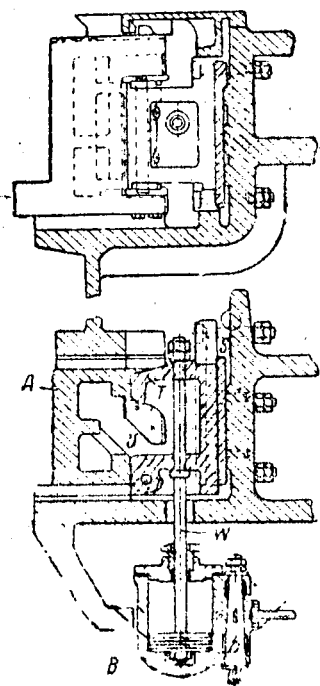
Общий вид кинематической передачи от вала к матрице
